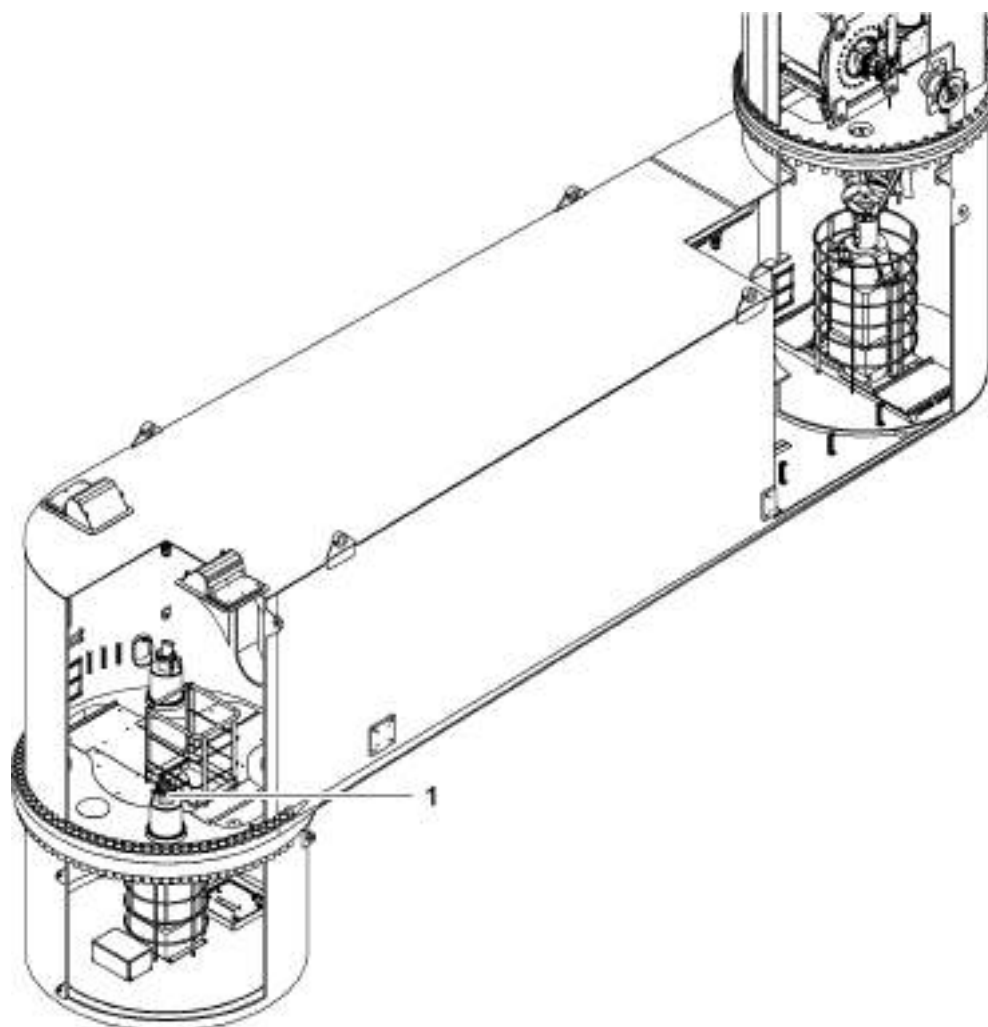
Llenado de aceite del brazo principal de mecanismo giratorio
